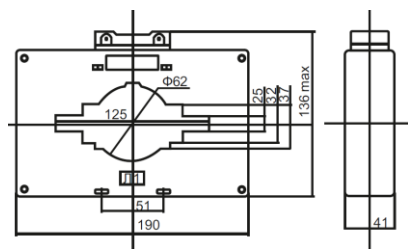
Габаритные и установочные размеры трансформаторов тока ТСП-0,66-120
